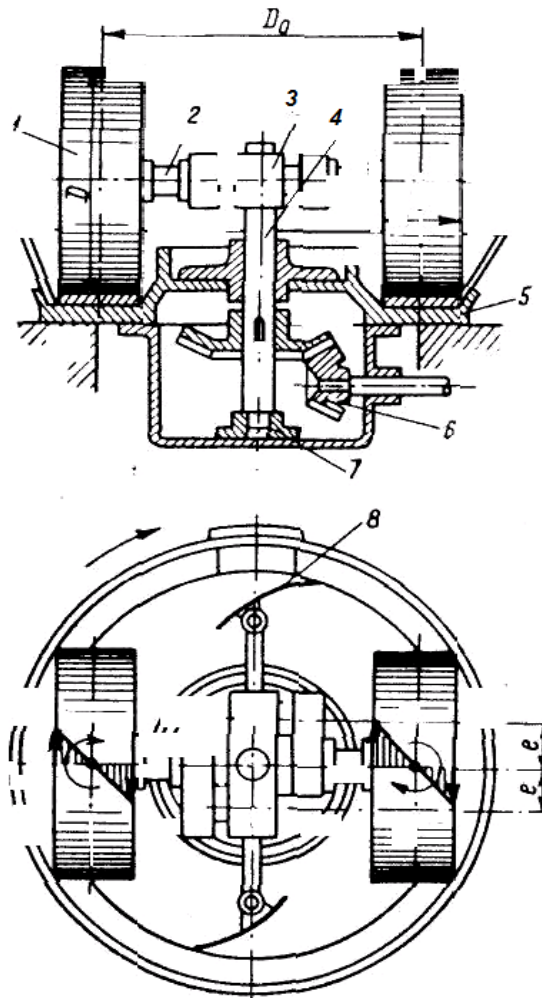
Бегуны: 1 – катки; 2 – полуоси катков; 3 – водило; 4 – центральный вал; 5 – чаша; 6 – коническая пара; 7 – подпятник; 8 – скребки
